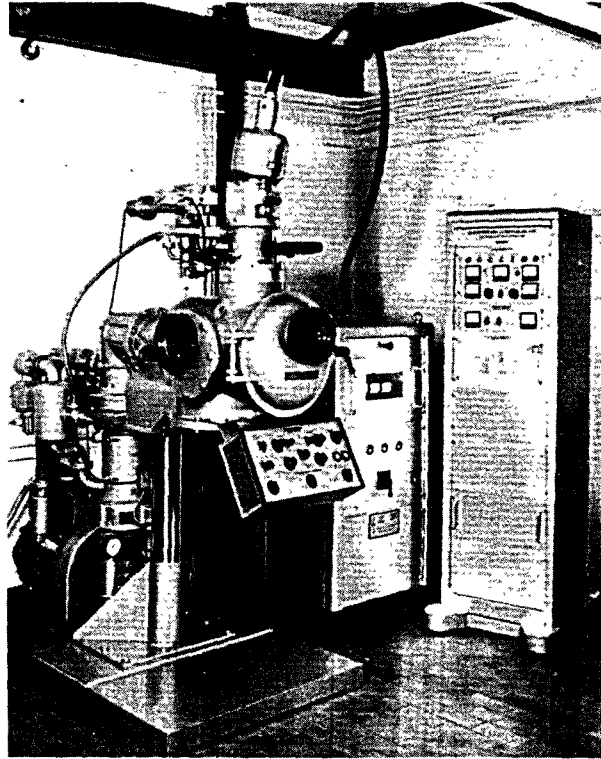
Elektronenstrahl-Schweißmaschine ESW 5 der Fa. Balzers
